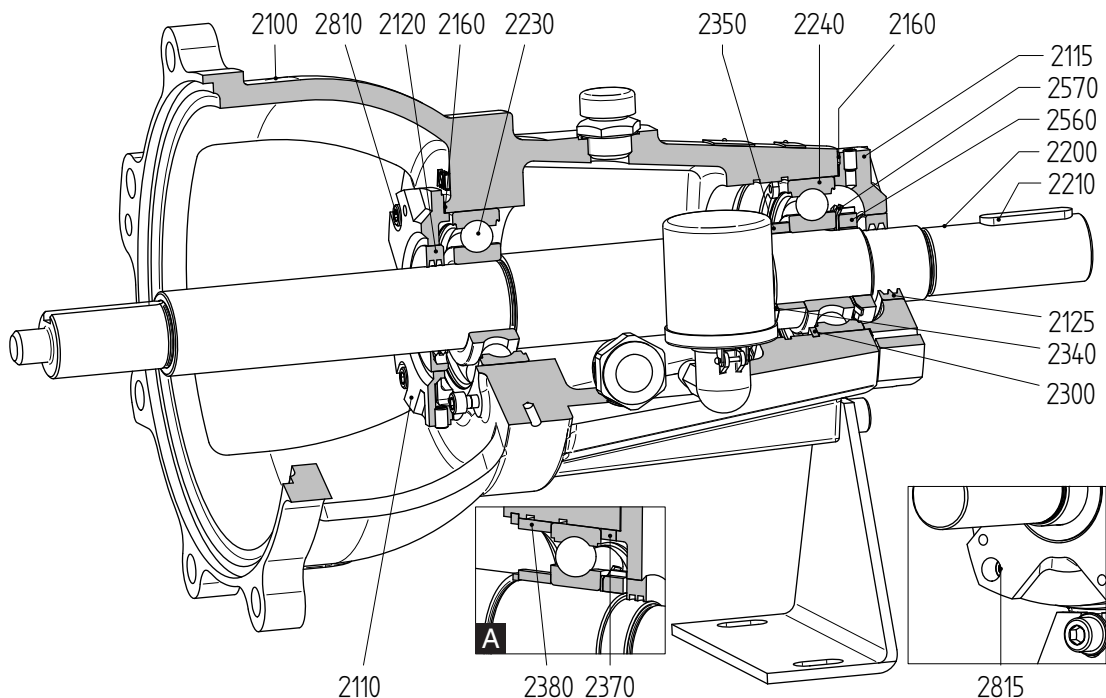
轴承 L3（标准，油润滑）（A = 轴承组 3）。
